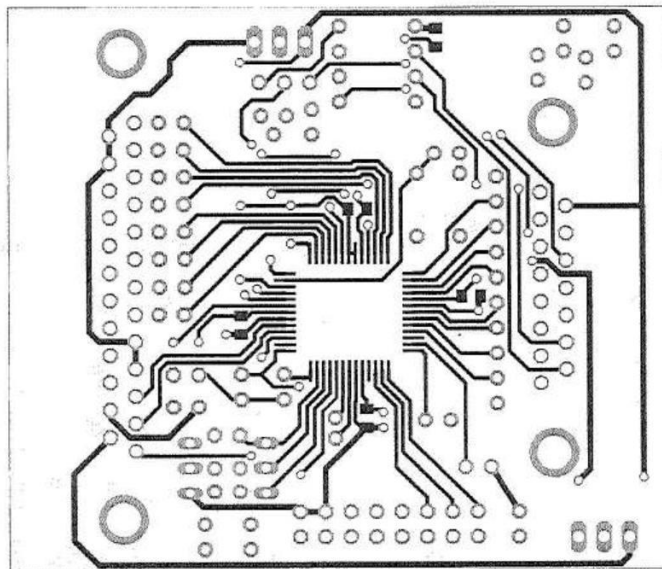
PCB:Tarjeta de adquisición, capa superior.
